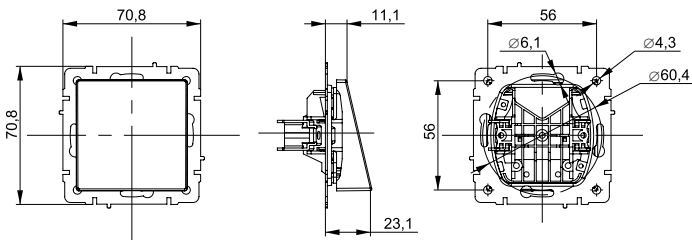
Габаритные и установочные размеры вывода кабеля / Figure 1 – Overall and installation dimensions of the
